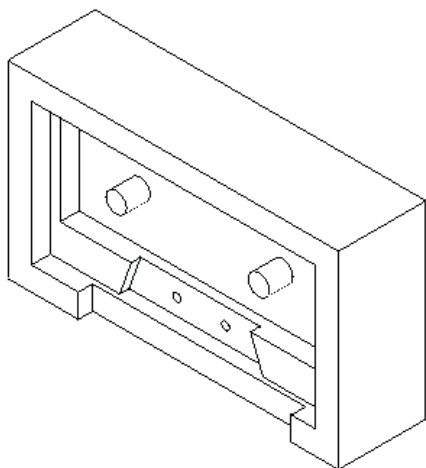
Деталь литейной формы для изготовления компакт-кассет
